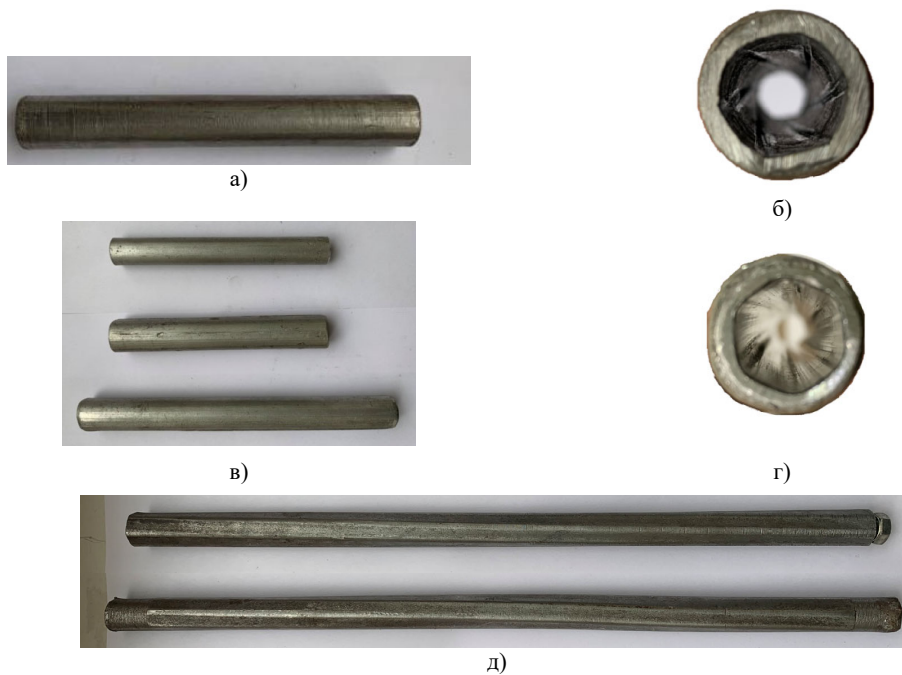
Деталі після обробки: а, в – вигляд зовнішньої циліндричної поверхні, Сталь 20, алюміній Д18 відповідно; б, г – внутрішня гвинтова поверхня, поперечний вид Сталь 45, алюміній Д18 відповідно; д – гвинтова оправка з профілем внутрішнього каналу
